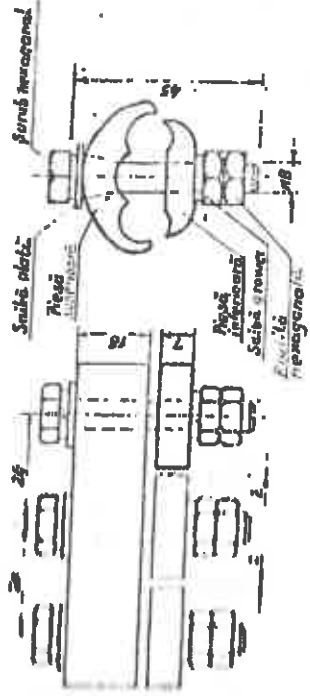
CLEMĂ UNIVERSALĂ U.A.
